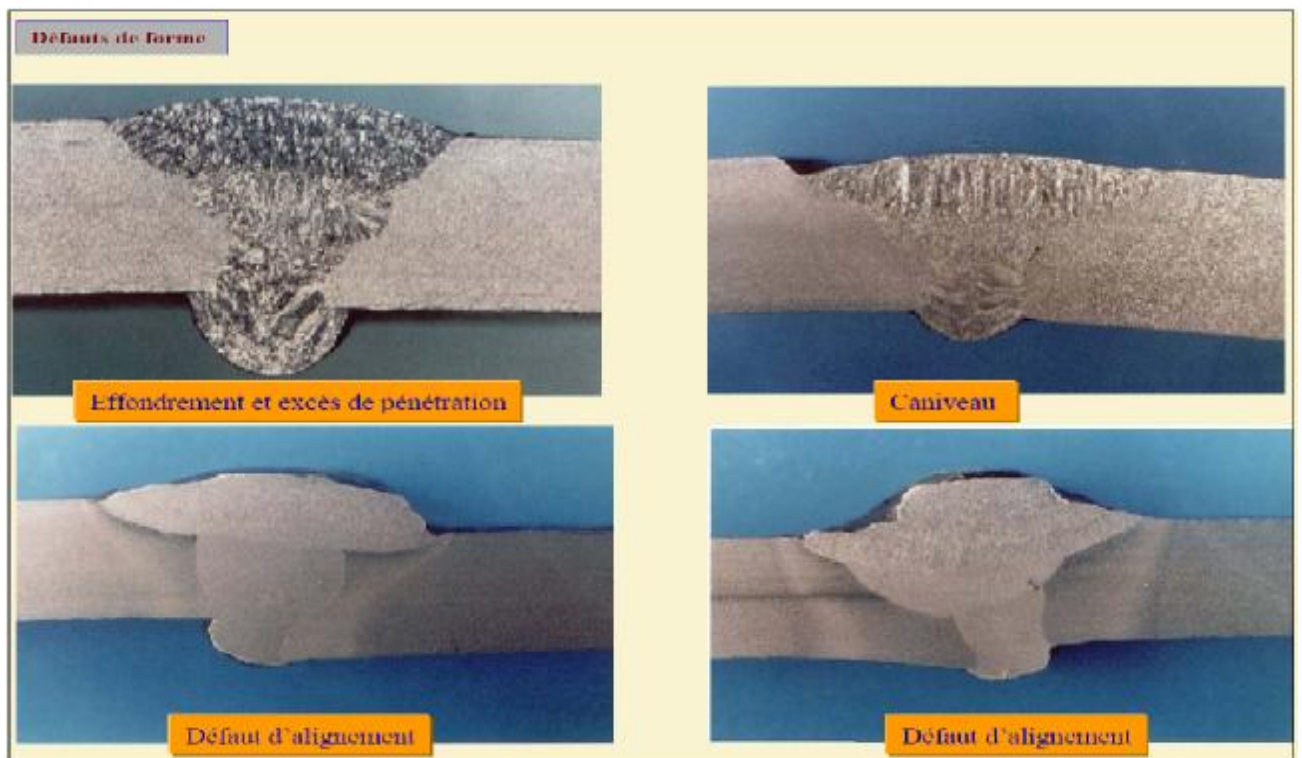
Défauts de forme de soudure pouvant être décelés par examen visuel
